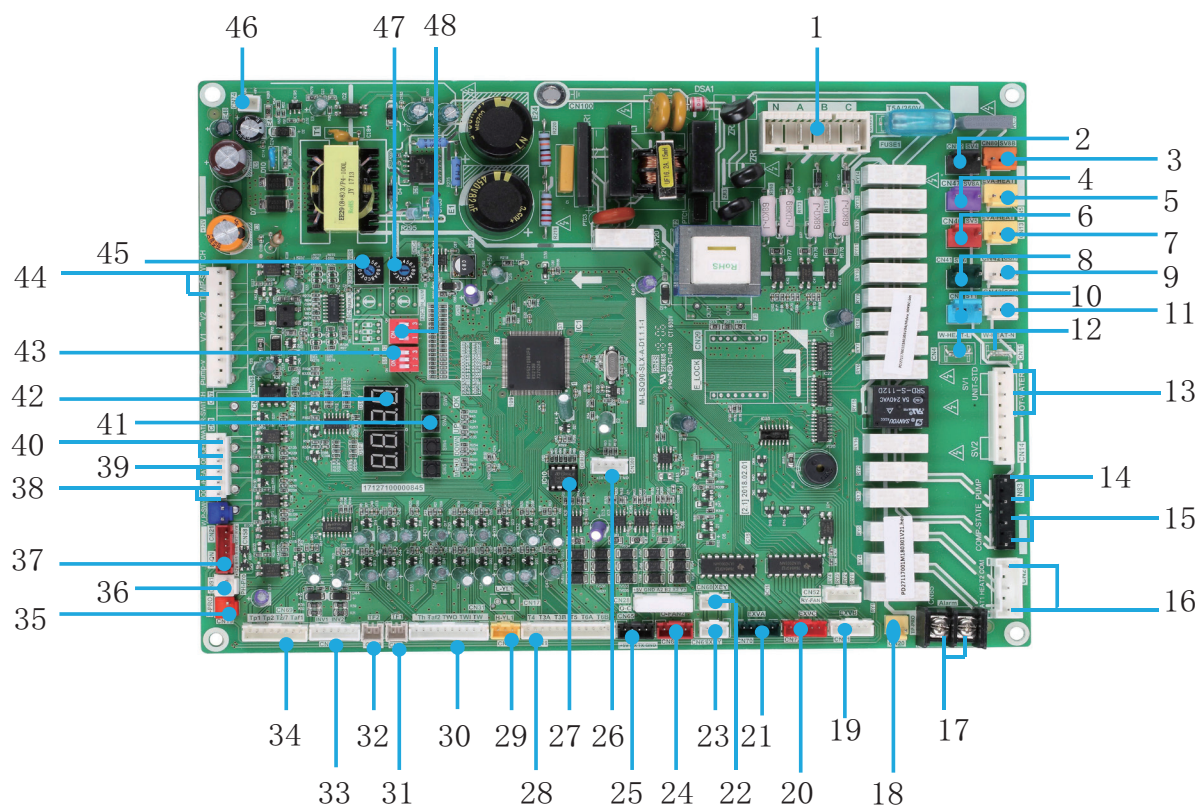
Blocul PCB principal KEM-90 DNS3
